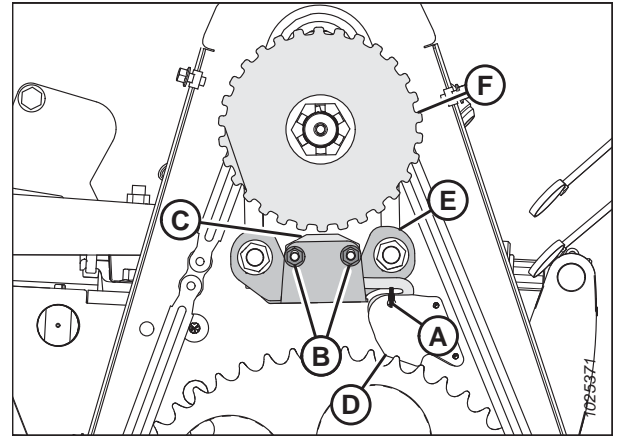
Haspelantriebsbaugruppe – Drehzahlsensor
